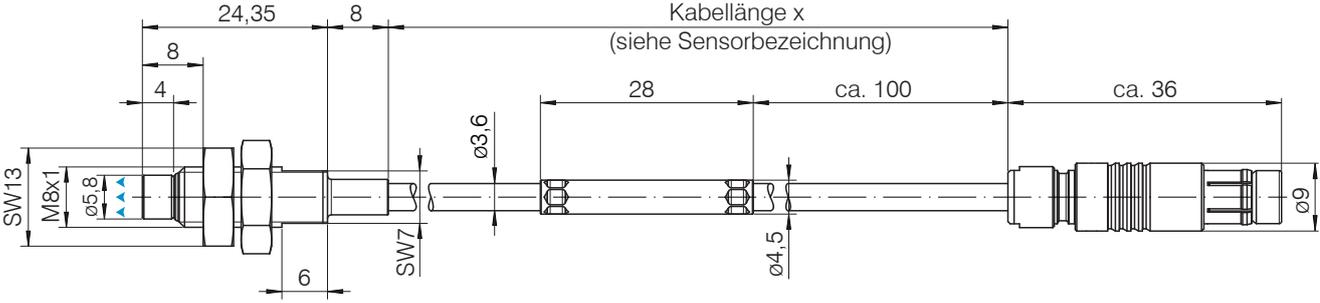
Maßzeichnung Sensoren ES-U2-C-CAX/mB0, Abmessung in mm
